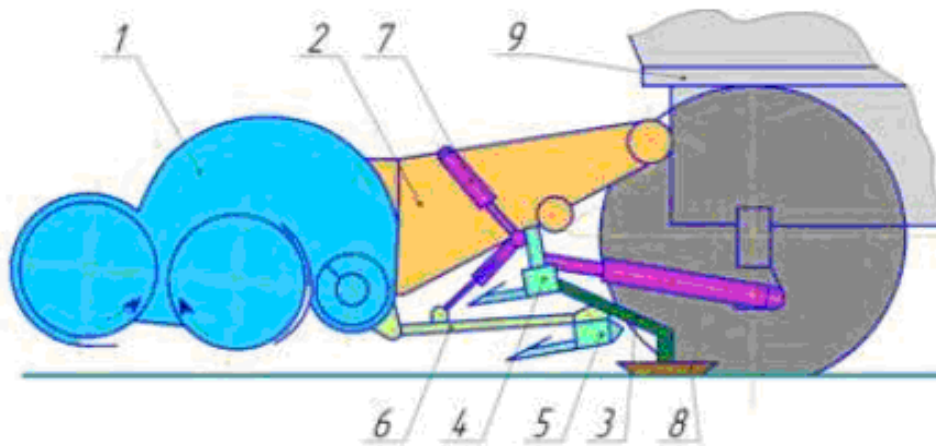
Пристрій до обчісувальної жатки для скошування стебел: 1 – обчісувальна жатка; 2 – похила камера комбайна; 3 – рама подрібнювального пристрою; 4 і 5 – верхній і нижній різальні апарати; 6 – тяга; 7 – гідроциліндр; 8 – башмак; 9 – зернозбиральний комбайн.
